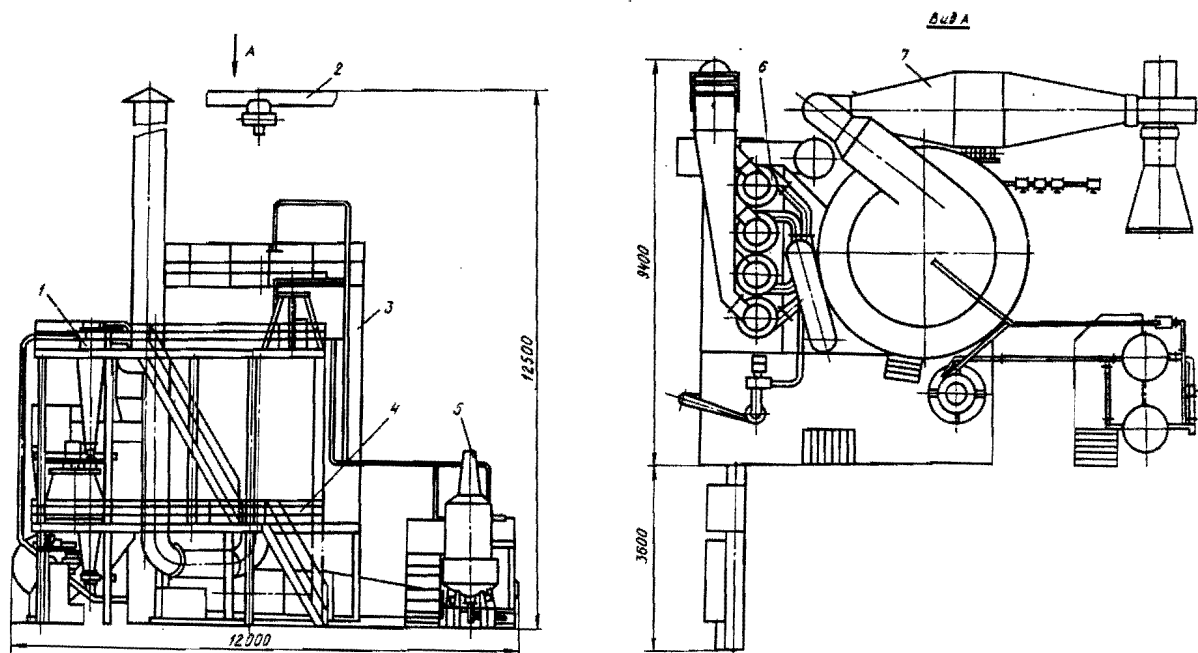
Общий вид установки распылительной сушильной марки А1-ОРЧ для молока:
